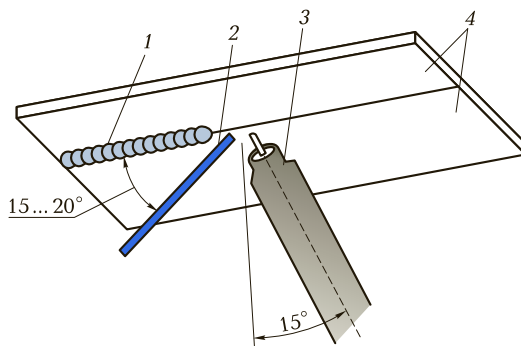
Положение горелки и присадочной проволоки при сварке в вертикальном положении:
